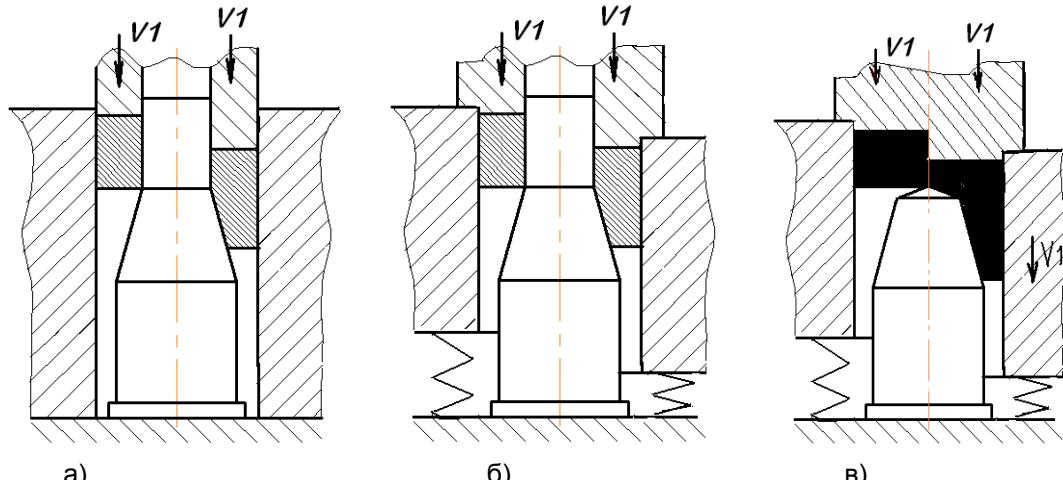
Деформирование кольцевых заготовок выдавливанием в зазор между неподвижными контрпуансоном и матрицей (а) и неподвижным контрпуансоном и подвижной матрицей (б); выдавливание сплошной заготовки в зазор между неподвижным контрпуансоном и подвижной матрицей (в)
